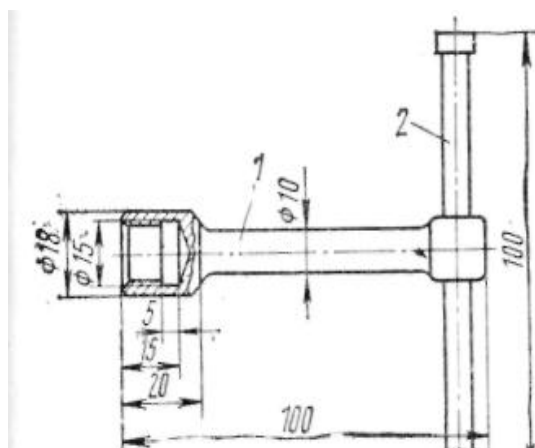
Ключ для вывертывания втулки штока толкателя из корпуса насоса:
